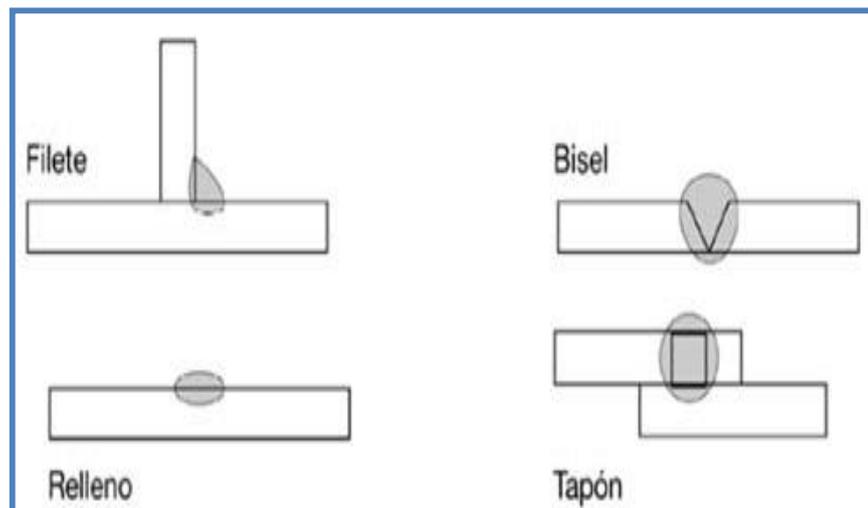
PRINCIPALES TIPOS DE SOLDADURA
